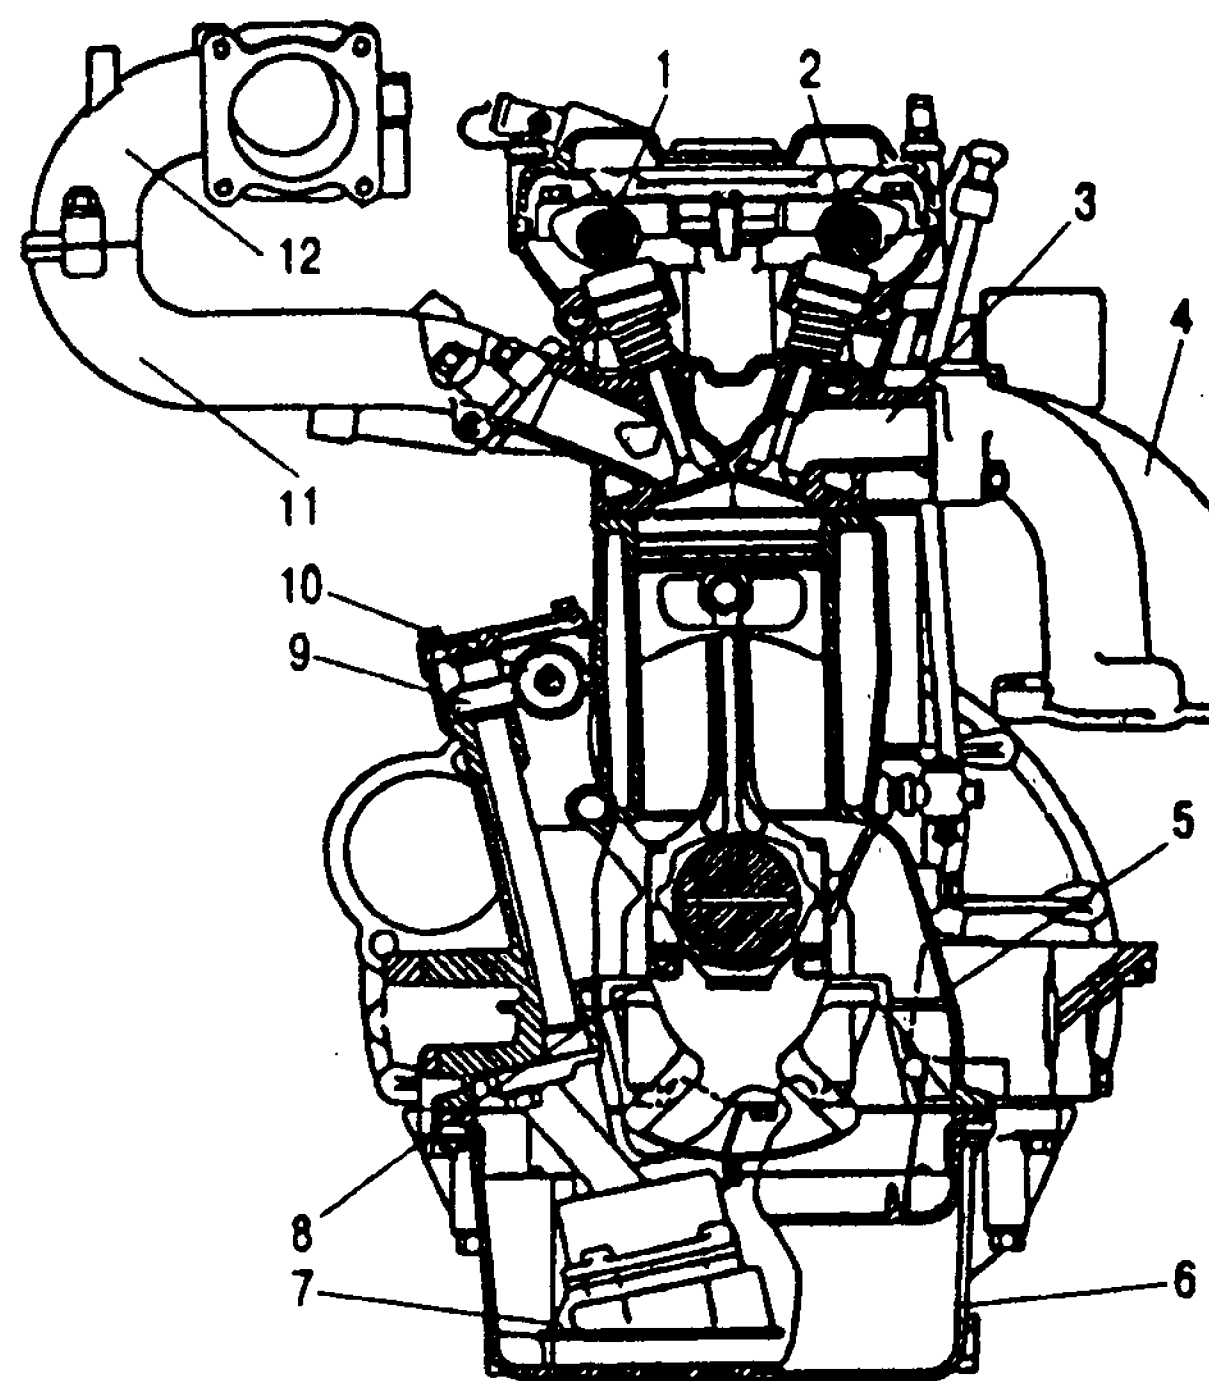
Поперечный разрез двигателя: 1 - распределительный вал впускных клапанов; 2 - распределительный вал выпускных клапанов; 3 - головка цилиндров; 4 - выпускной коллектор; 5 - блок цилиндров; 6 - масляный картер; 7 - масляный насос; 8 - коленчатый вал; 9 - шестерня привода масляного насоса ведомая; 10 - шестерня привода масляного насоса ведущая; 11 - впускная труба; 12 - ресивер
